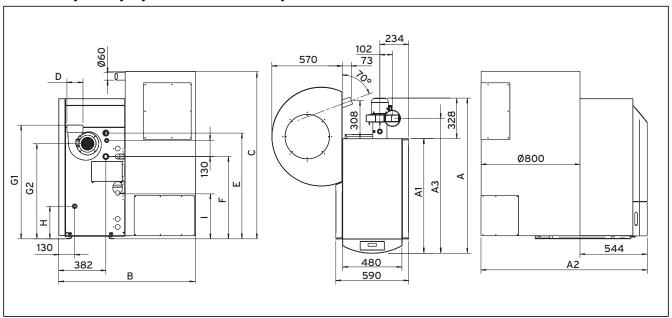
Abmessungen: Pelletkessel mit Saugaustragung oder Handbeschickung
